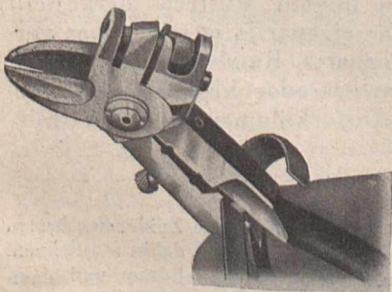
Stahlbauzange zu Hellers Stahlbaukasten, beim „Rollen“ eines Bauteils
